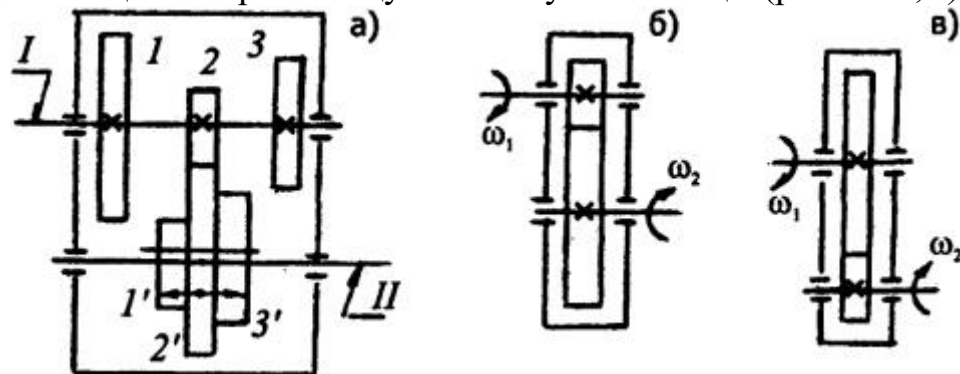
Коробка перемены передач (а), редуктор (б) и мультипликатор (в)
